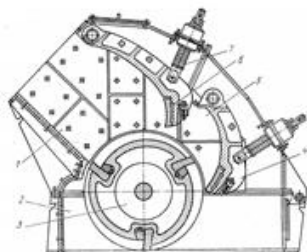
Роторная дробилка:1-верхний корпус;2- нижней корпус;3- ротор;4- отражательная плита;5 -износостойкие плиты; 6- сменные плиты; 7- предохранительно-регулирующее устройство.
